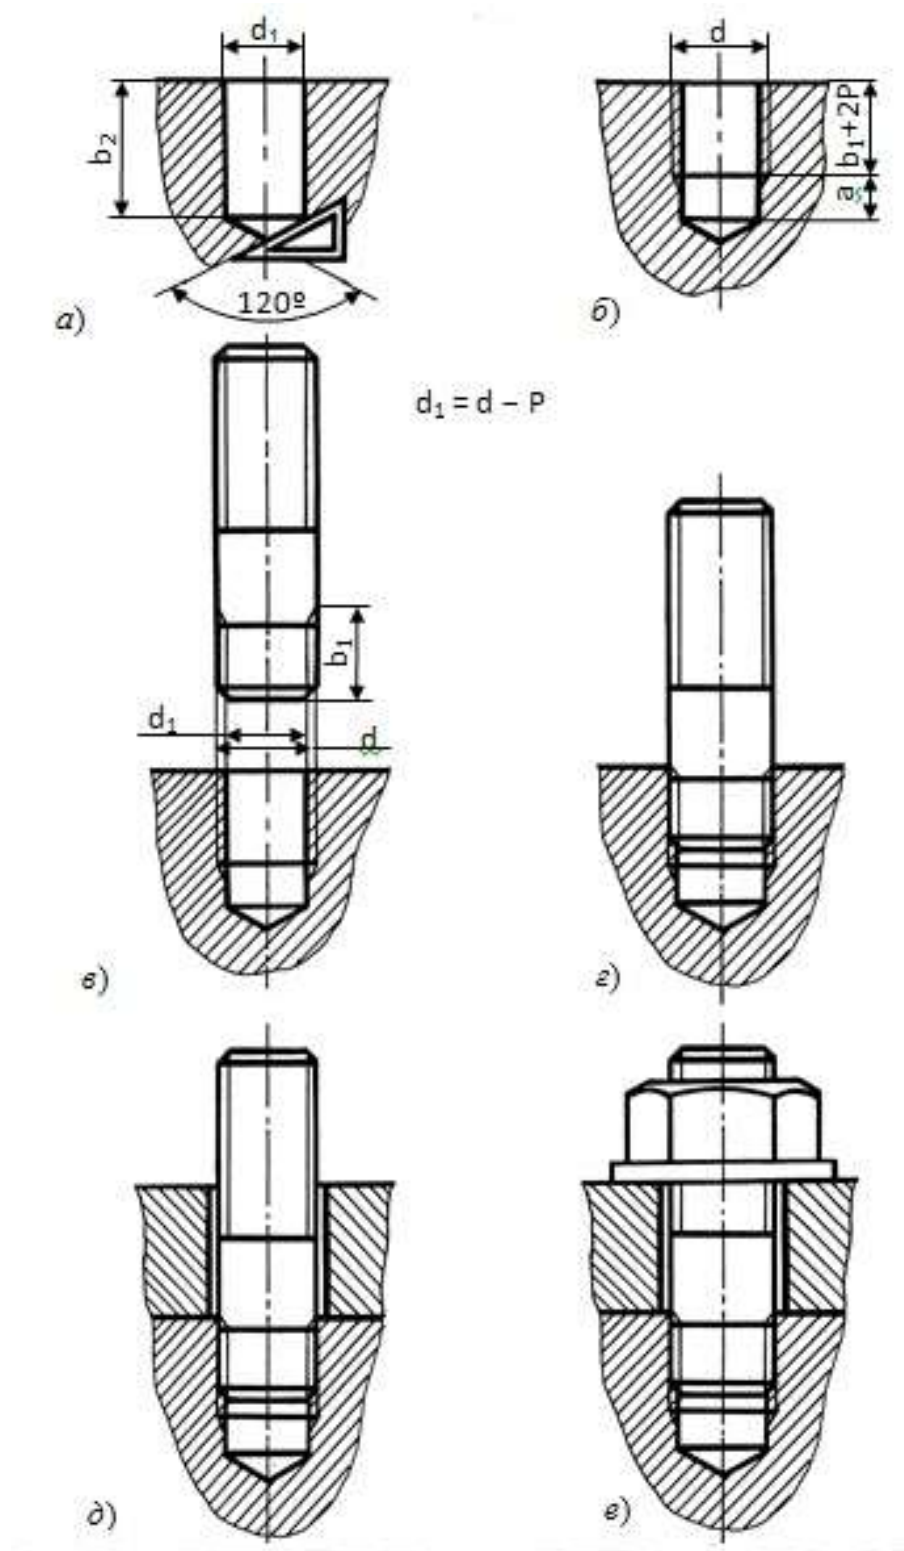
Технологическая последовательность выполнения отверстия с резьбой под шпильку и порядок сборки шпильчного соединения
